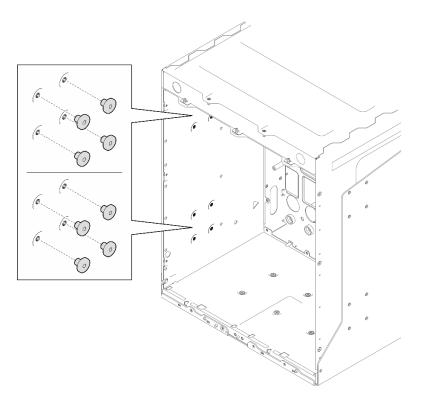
Extracción de los tornillos del lado interno izquierdo del alojamiento
